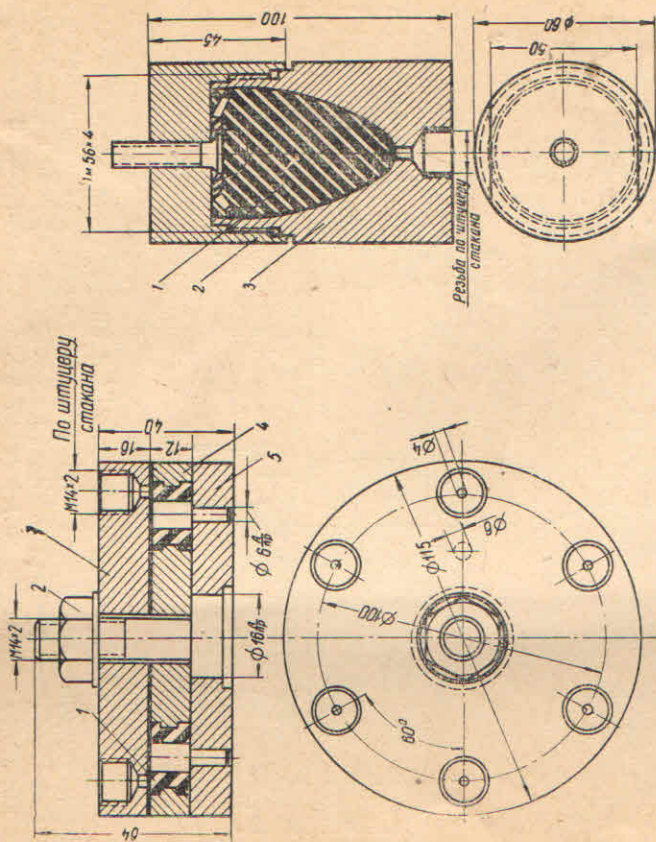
Пресс-форма в сборе с деталями № 20—1703045 — подушка противопушная рычагов переключения передач: 1 — деталь № 20—1703045; 2 — гайка стяжной шпильки; 3 — верхняя часть; 4 — средняя часть; 5 — основание
